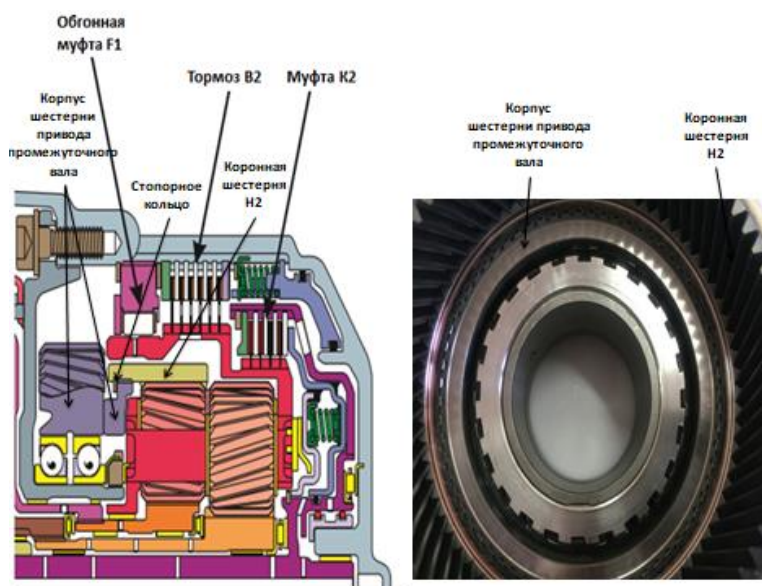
Устройство корпуса шестерни привода промежуточного вала
